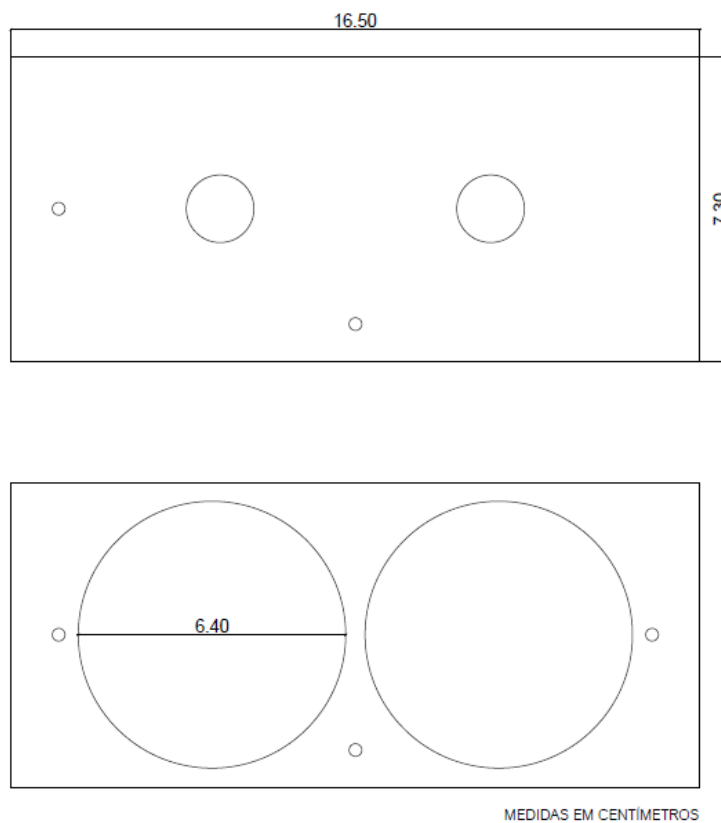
Desenho técnico do módulo de ultracondensadores.
